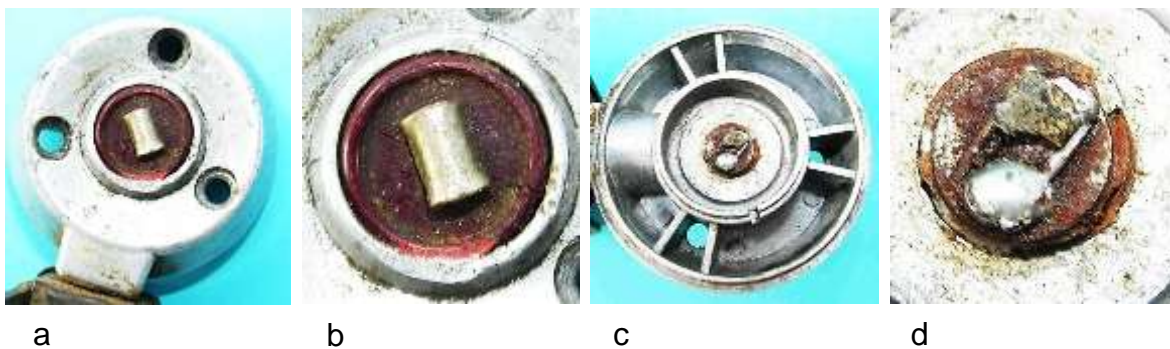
Boden mit Kabelanschluss: a) und b) Unterer Bogen des Kontaktbügel zur Befestigung des Kabels, c) und d) Splintlappen des Kontaktbügels mit Lötstellen
